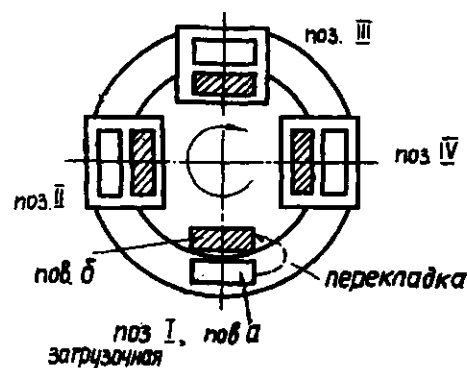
Схема обработки отверстий с двух сторон при перекладывании заготовок в двухместном приспособлении
